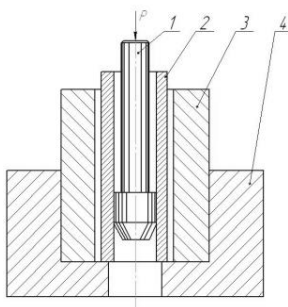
Схема восстановления цилиндрической детали раздачей: 1 – прошивка; 2 – поршневой палец; 3 – матрица; 4 – основание матрицы
